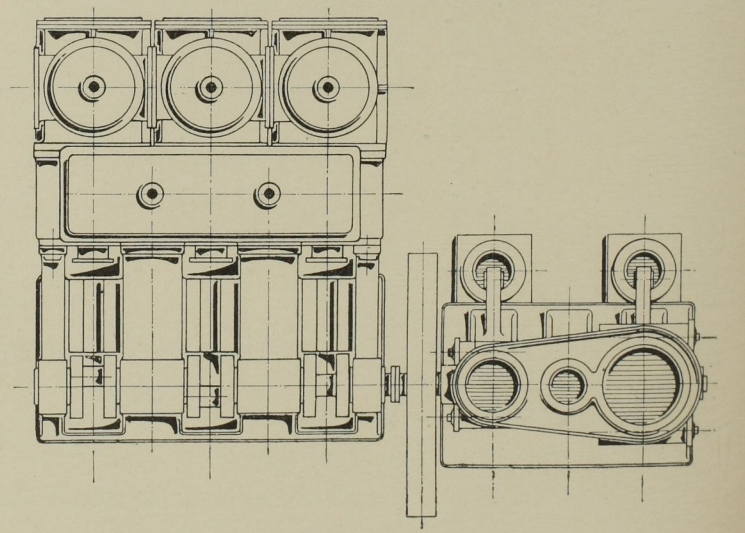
Grundriss. Masst. 1:90.
